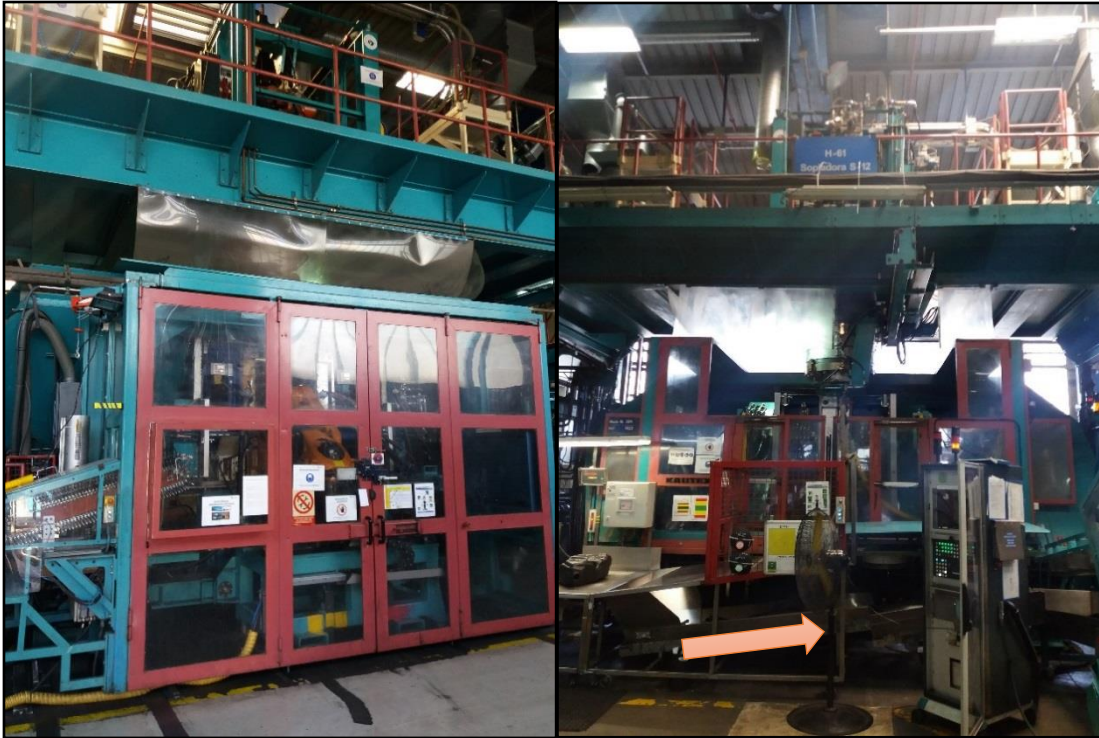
Parte trasera sopladora (izquierda) con el robot de colocación de bayoneta y parte delantera (derecha) con la cinta del molino para las coladas. (fuente: elaboración propia)
